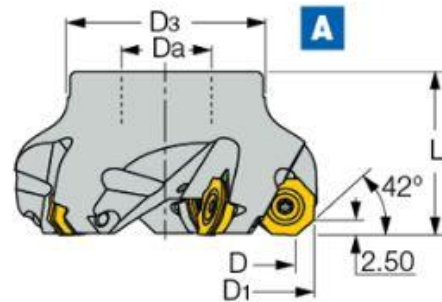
Freză frontală HOF D050-04-22-R06 [5]
